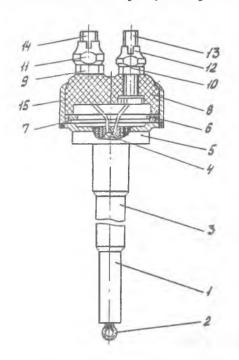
Рис. II. Конструктивная схема термопары Т-II2: I — втулка;2 — термоэлектролы; 3 — штуцер; 4 — керамическая трубка; 5 — корпус; 6. 7 — шайба; 8 — изолятор; 9, 10 — гайка; II, I2 — гайка само-контрящаяся; I3, I4 — винт; I5 — кожух
